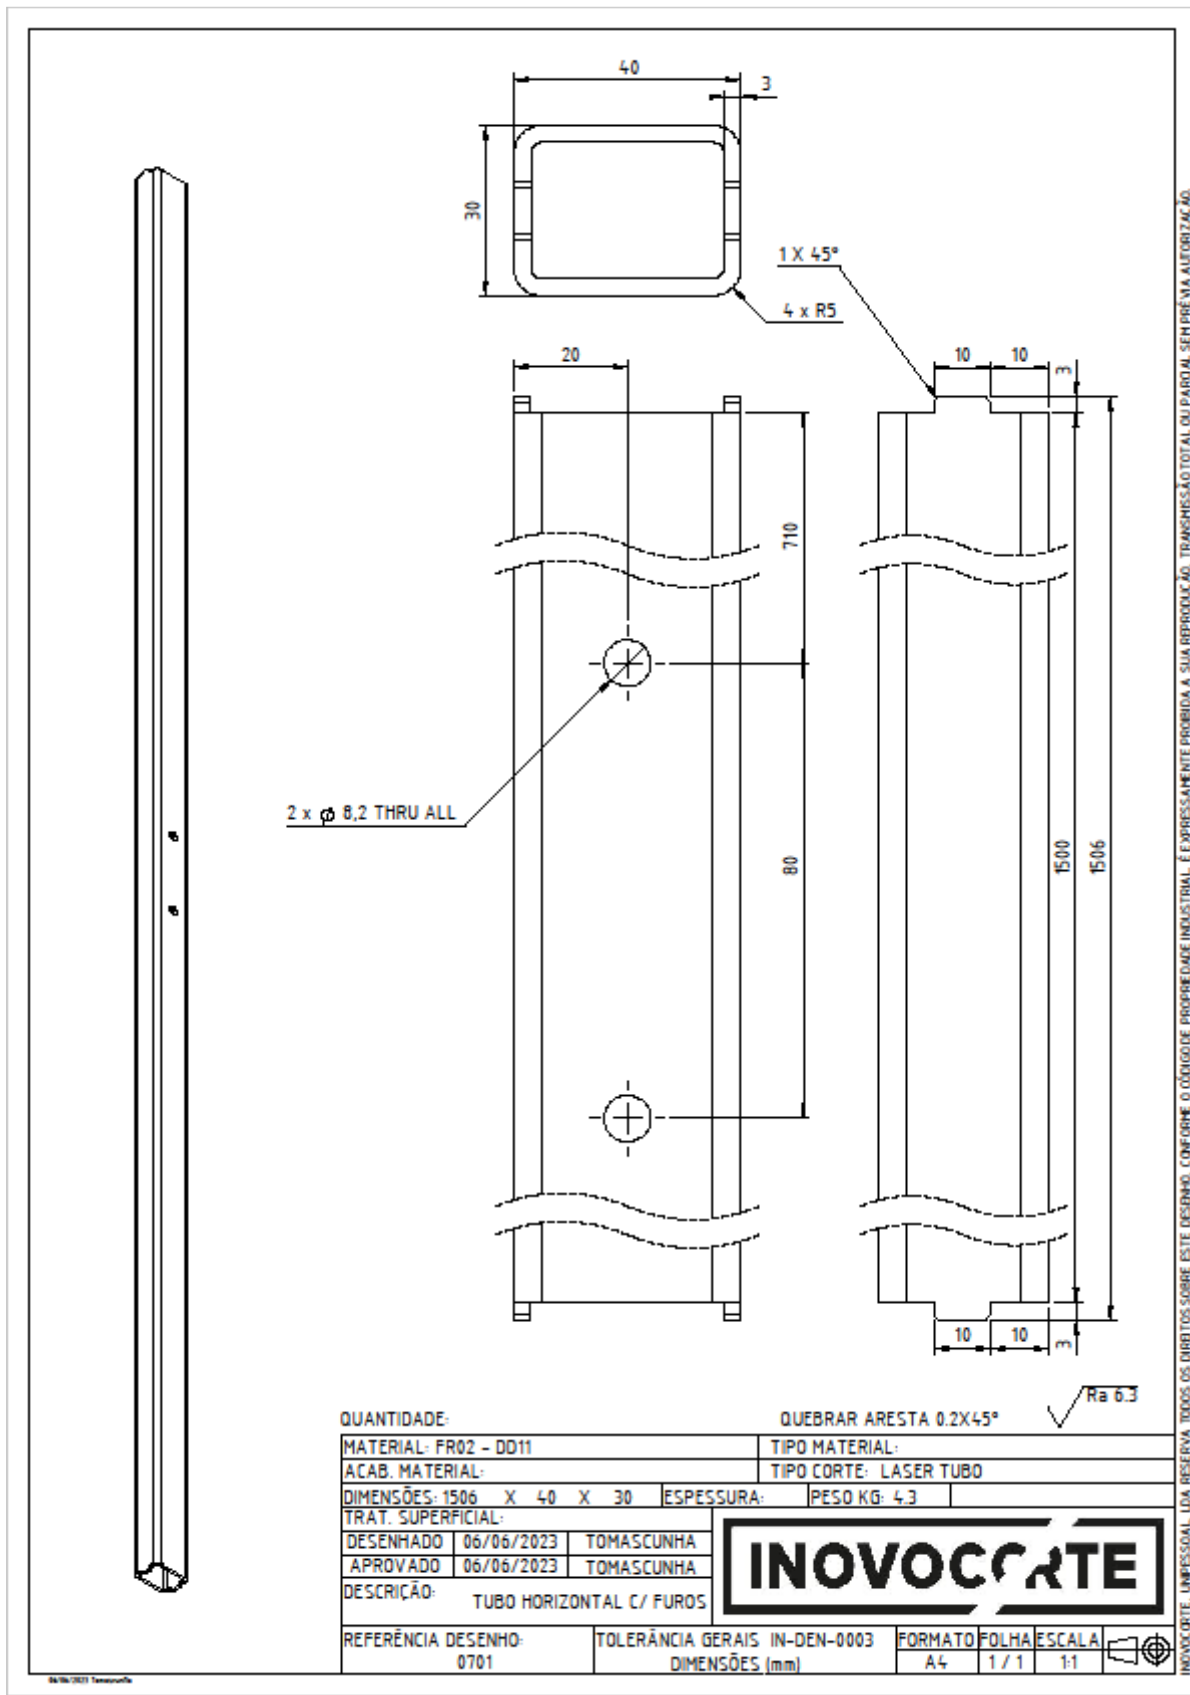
Desenho técnico do tubo horizontal com furos (0701).
